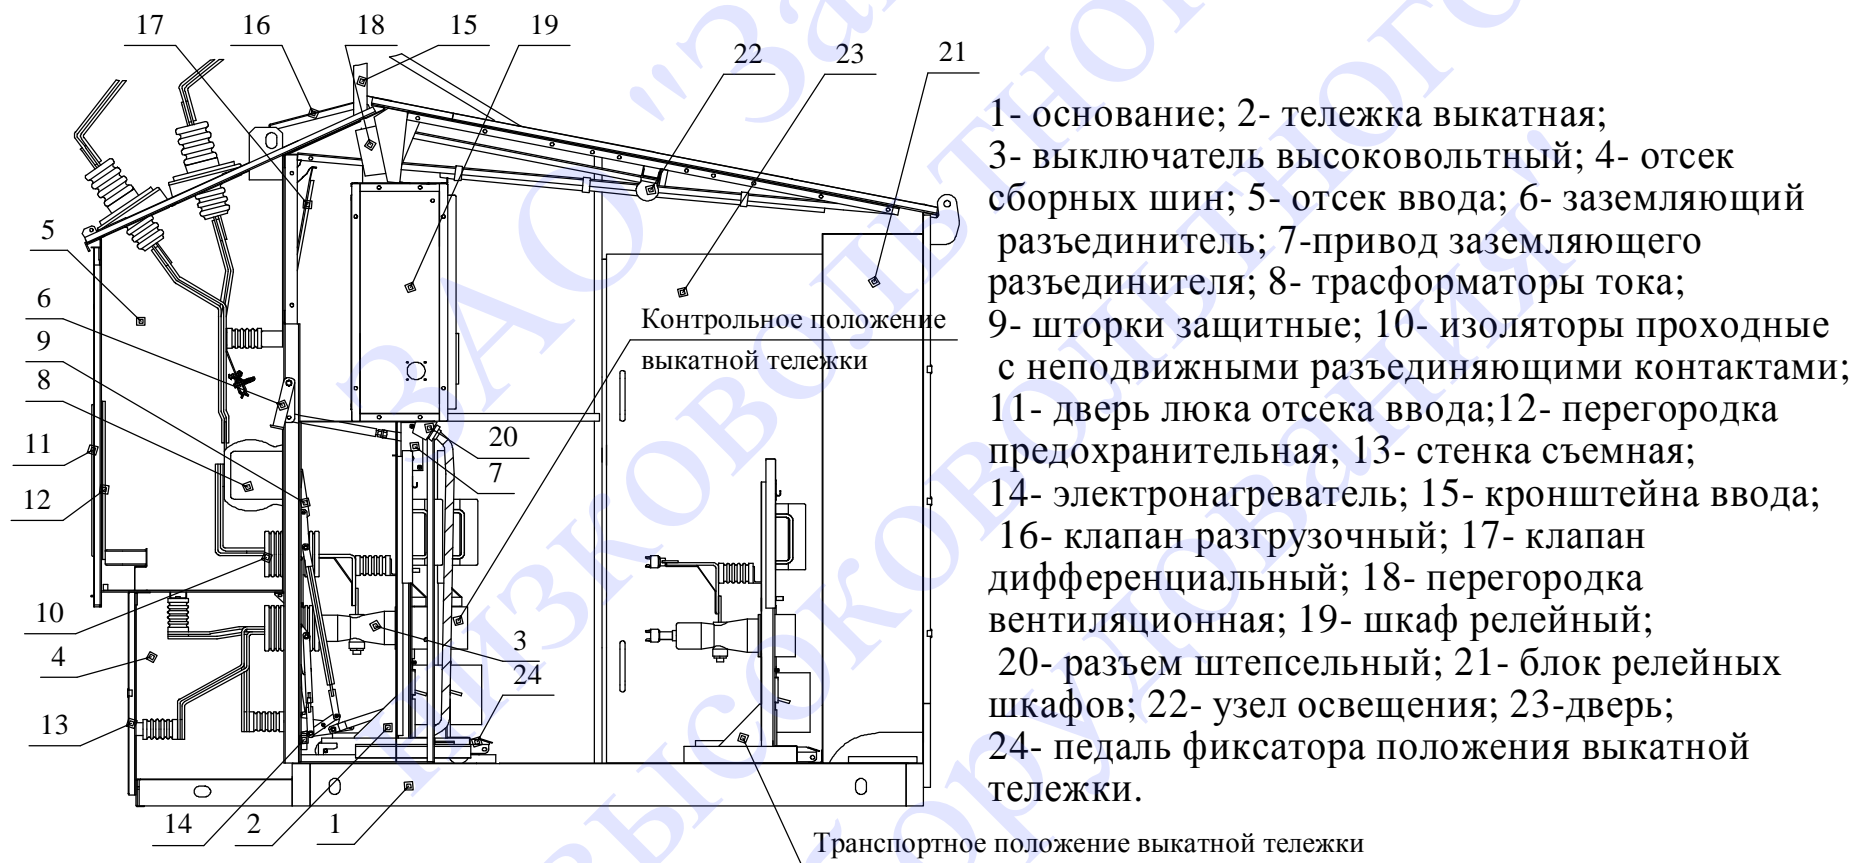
Блок КРУН исполнения У1 (Разрез по ячейке на 1600 А с воздушным вводом (выводом))
